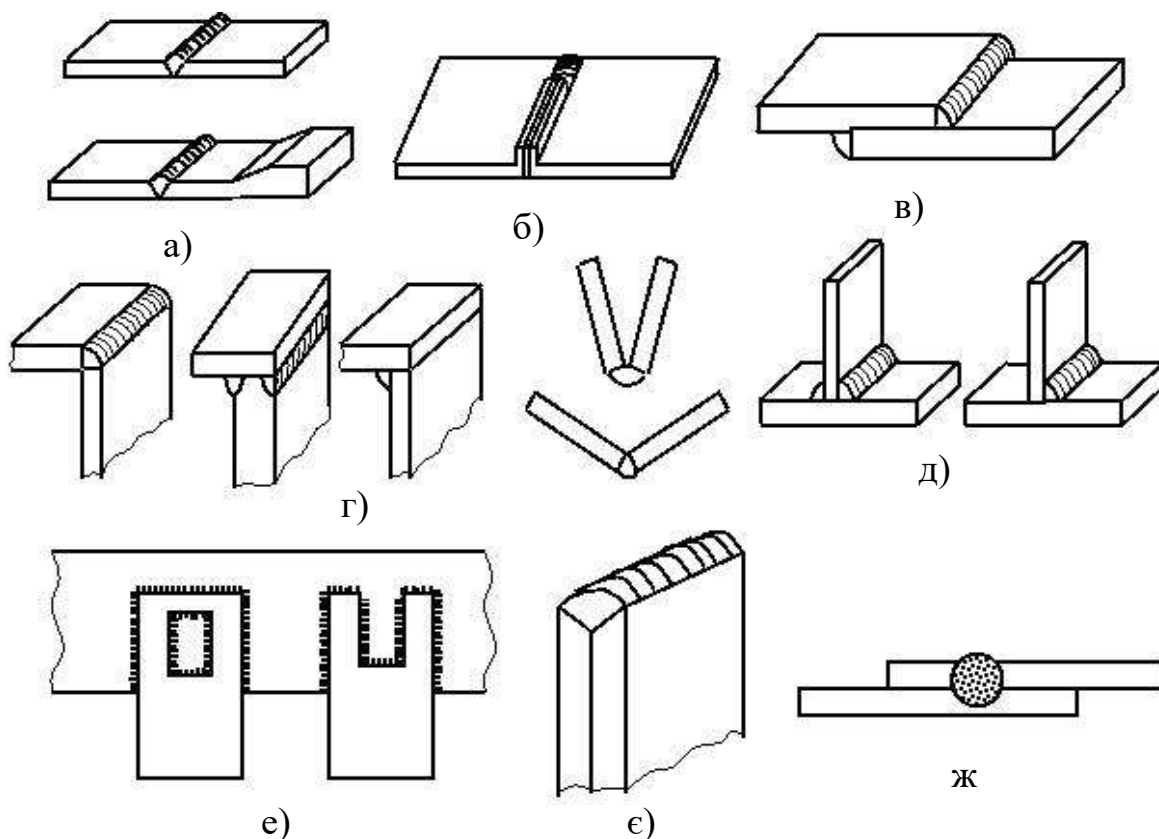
Види з'єднань складових зварних заготовок: а, б) стикові; в) внапуск; г) кутові; д) таврові; е) прорізи; е) торцеві; ж) електрозаклепочні
